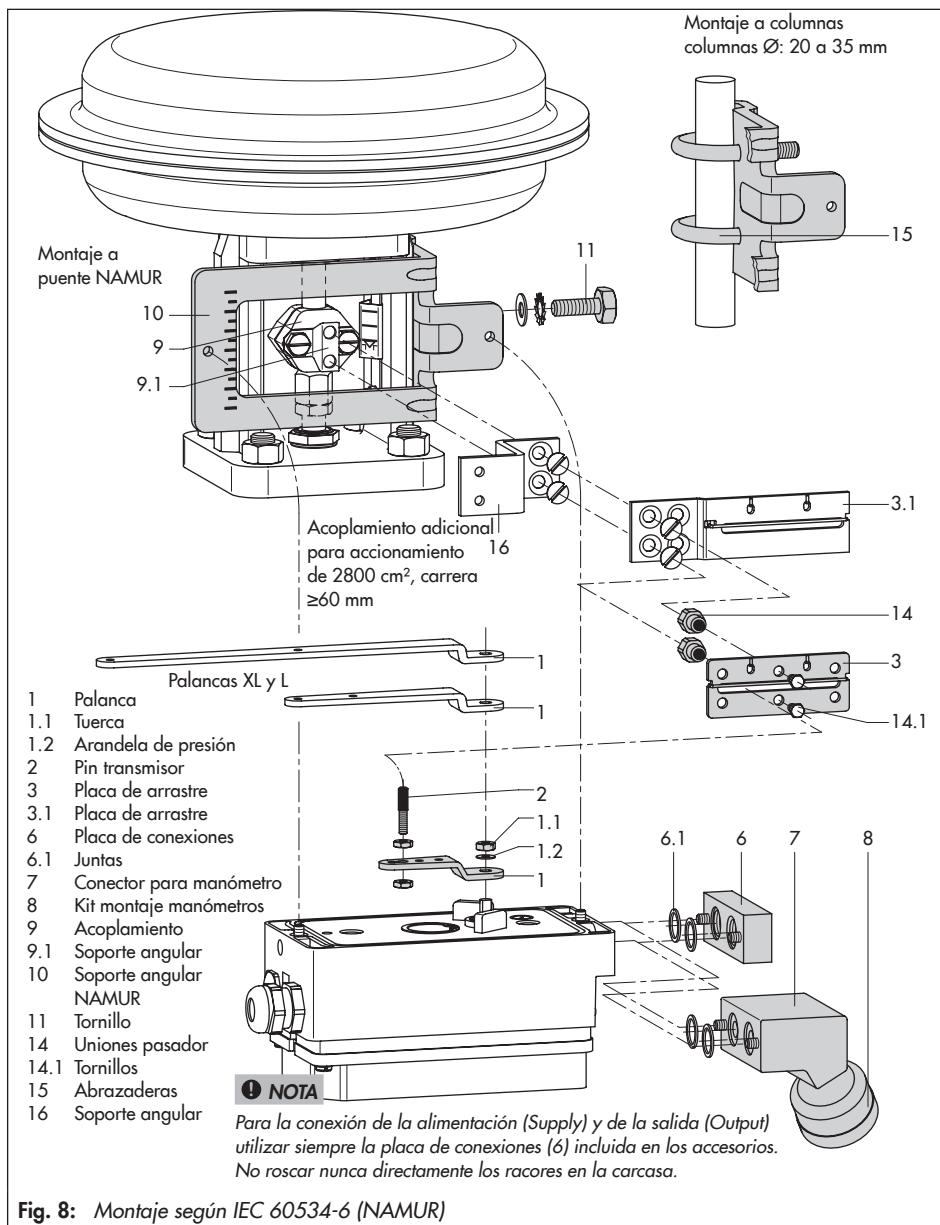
Montaje según IEC 60534-6 (NAMUR)
